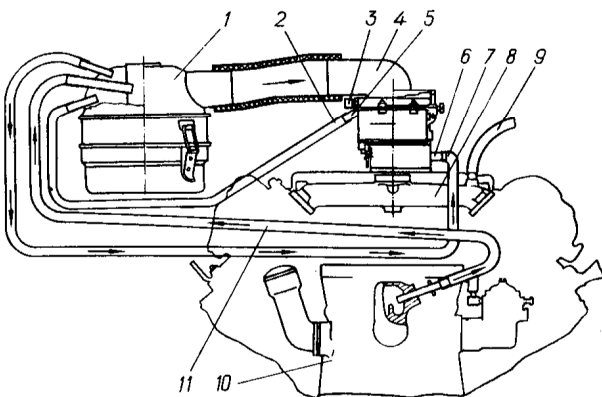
Схема отсоса картерных газов и разбалансировки поплавковой камеры карбюратора:
